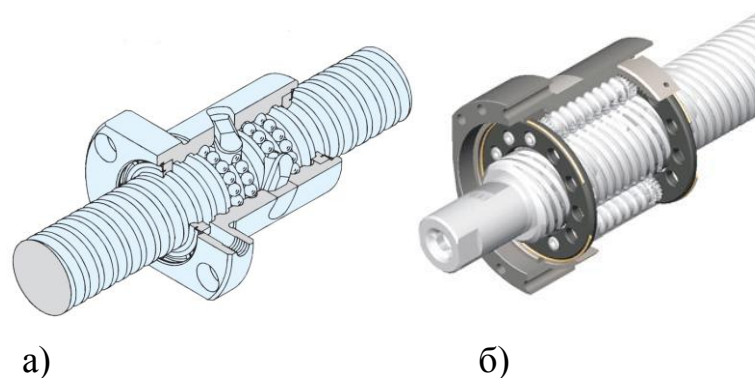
Передача гвинт гайка кочення: а-кулькова; б-роликова
